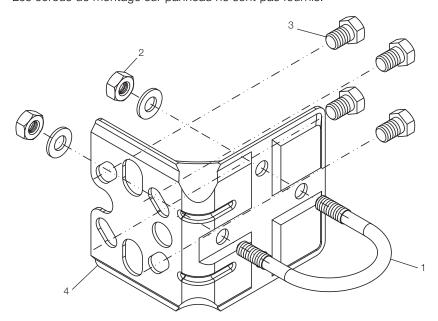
Kit support de montage mural ou sur tuyau (B2)
